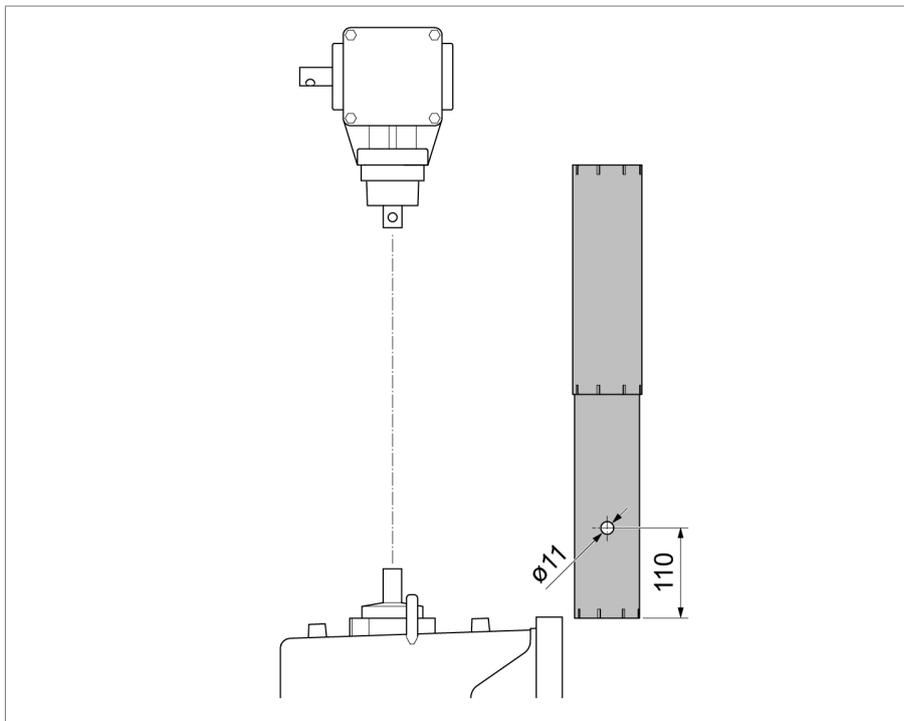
esecuzione del foro di messa a terra nel tubo di protezione telescopico
